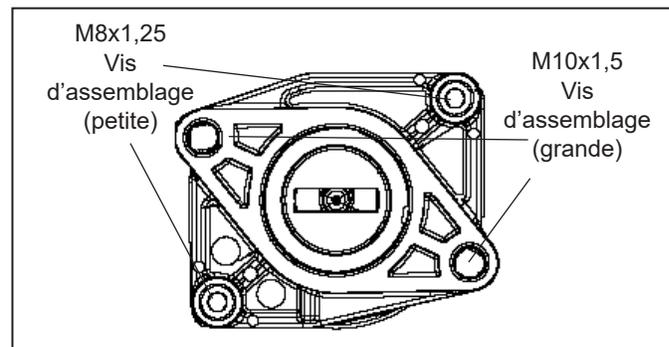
Boulons de fixation du couvercle d'extrémité arrière
